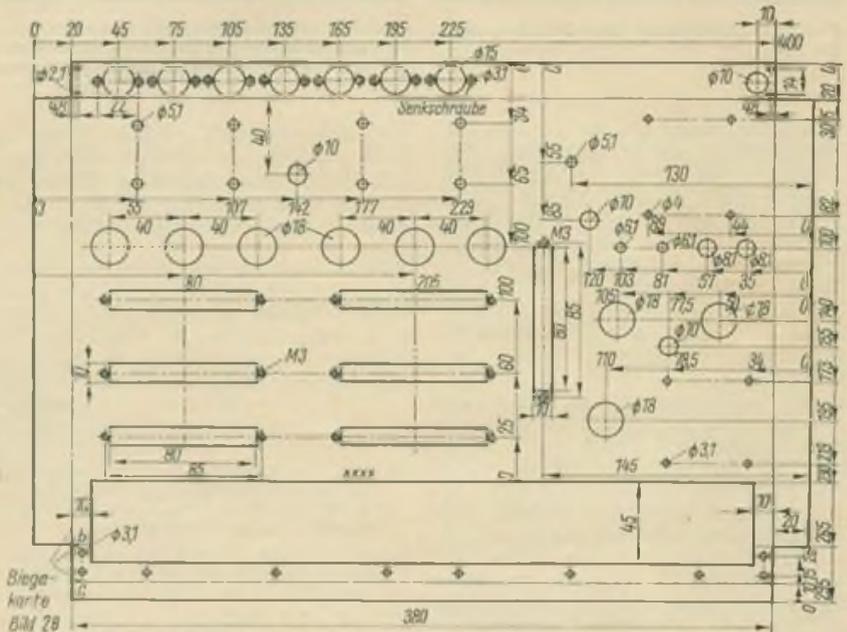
Die Abmessungen des Chassisbleches für den Verstärker
